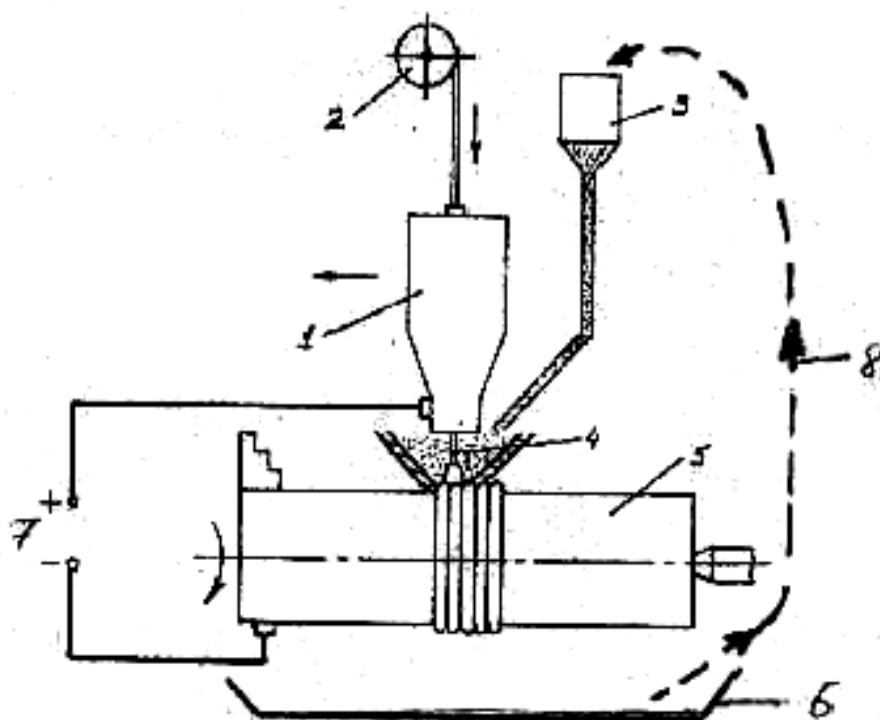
Схема наплавки деталей под слоем флюса:
